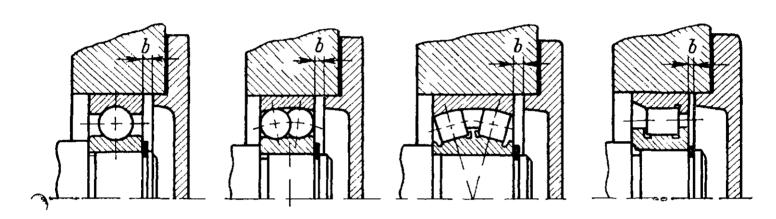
Некоторые конструктивные варианты шарнирно-подвижных опор валов с подшипниками качения
